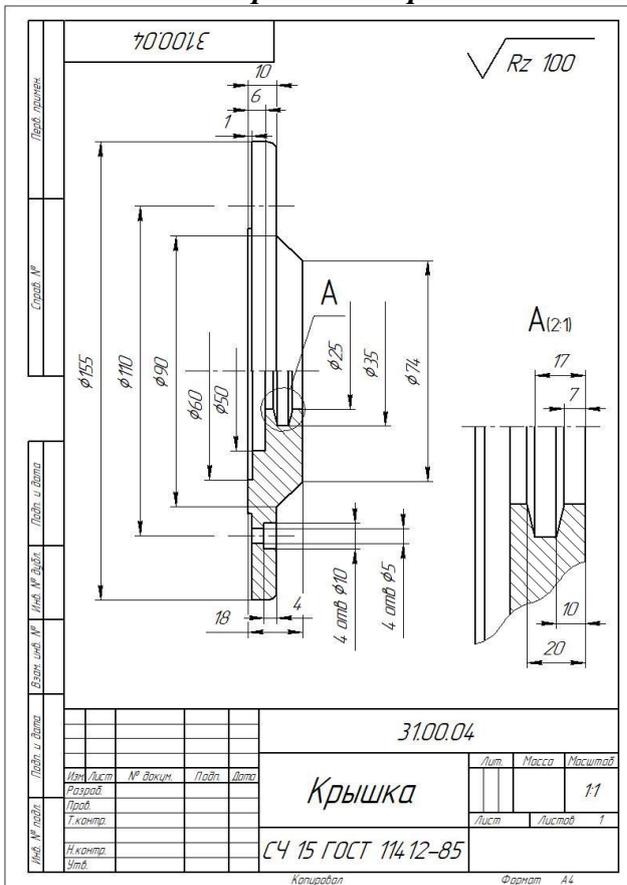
Образец выполнения задания КГ 3.4: рабочий чертёж
